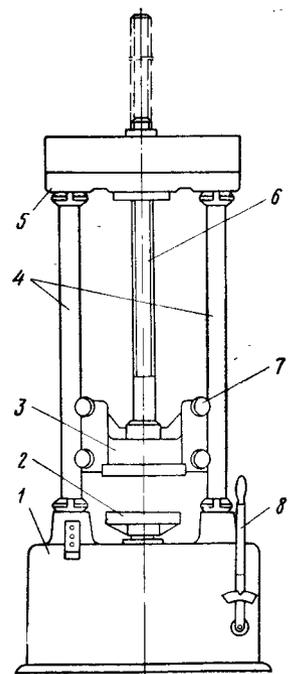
Винтовой пресс для запрессовки секций в пакеты
